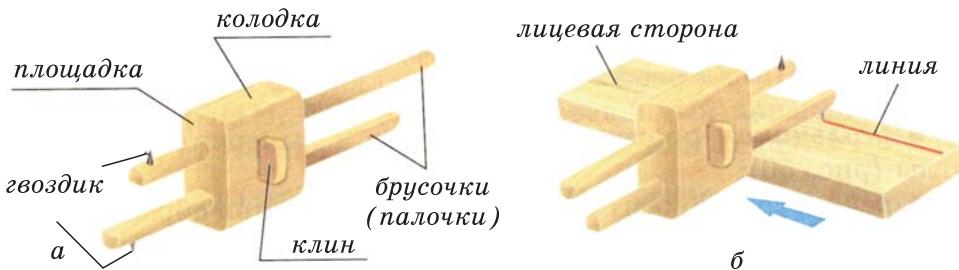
Рейсмус: а – основные части рейсмуса; б – разметка доски
